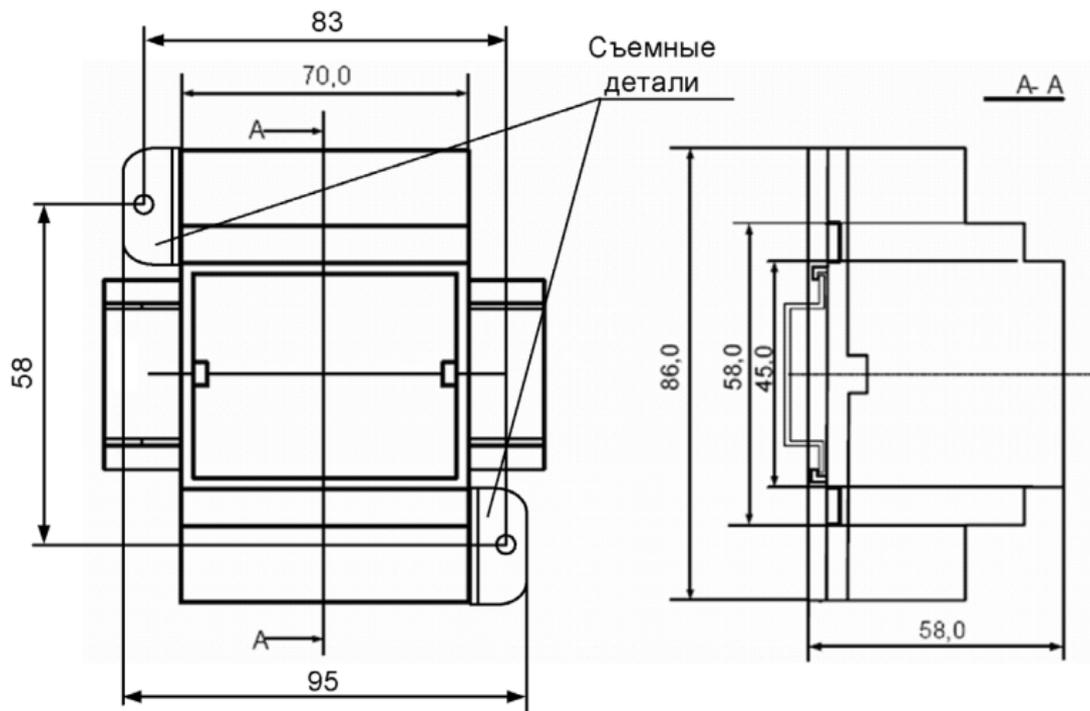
Габаритные и присоединительные размеры блока питания PSM-36-24
